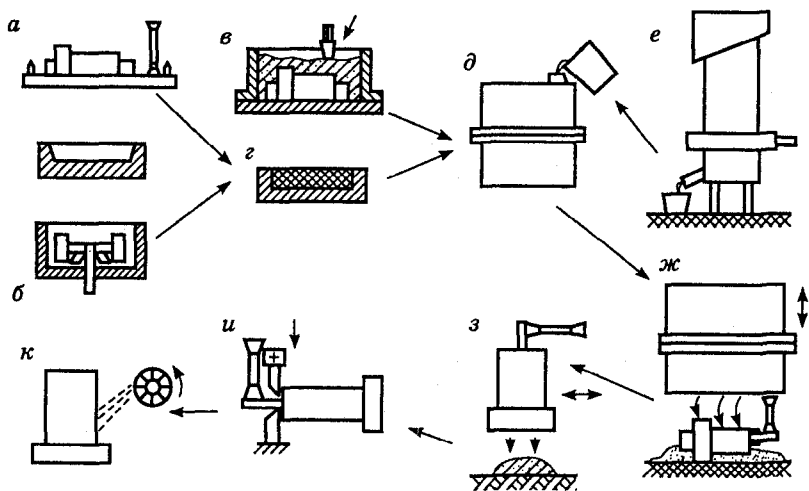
Последовательность операций изготовления отливки: а — изготовление модельного комплекта; б — приготовление смесей; в — изготовление формы; г — изготовление стержня; д — сборка и заливка формы; е — выплавка сплава; ж — выбивка формы; з — удаление стержня; и — обрубка литников; к — очистка
